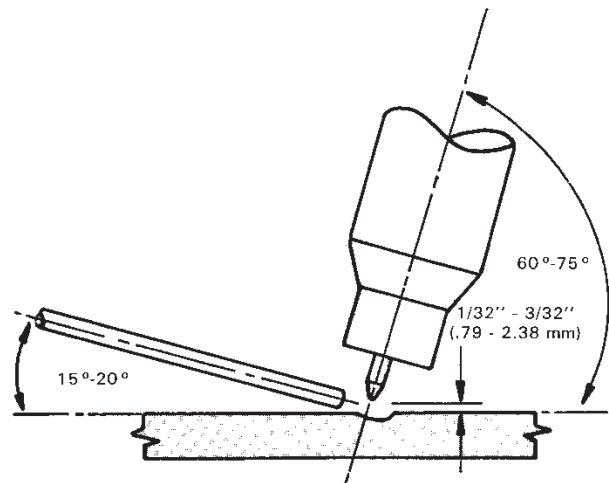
Posición relativa del electrodo y el metal de aporte en soldaduras GTAW.
